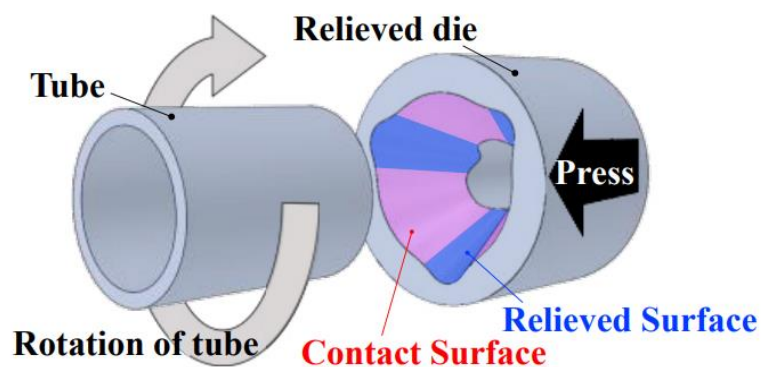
Схема процесу обтискання трубчастої заготовки обкочуванням конічною переривчастою матрицею [28]
